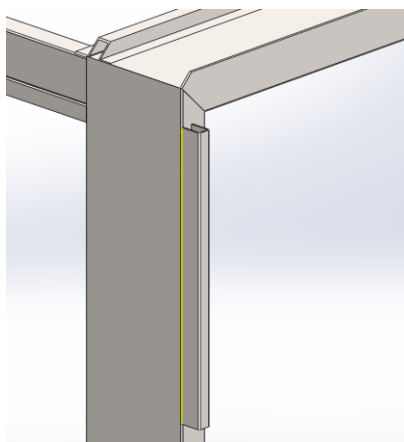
Detalle de soldadura de protector marco trasero
